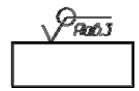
Обозначение одинаковой шероховатости поверхностей образующих замкнутый контур
